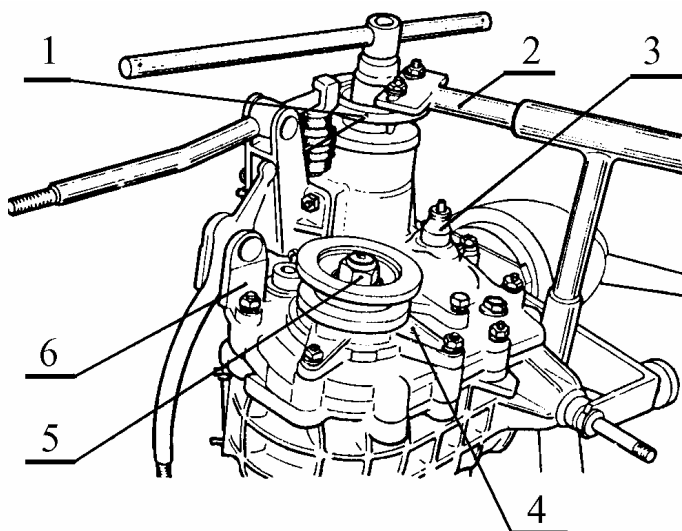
Отворачивание гаек крепления фланцев ведущего вала и вала привода переднего моста:
